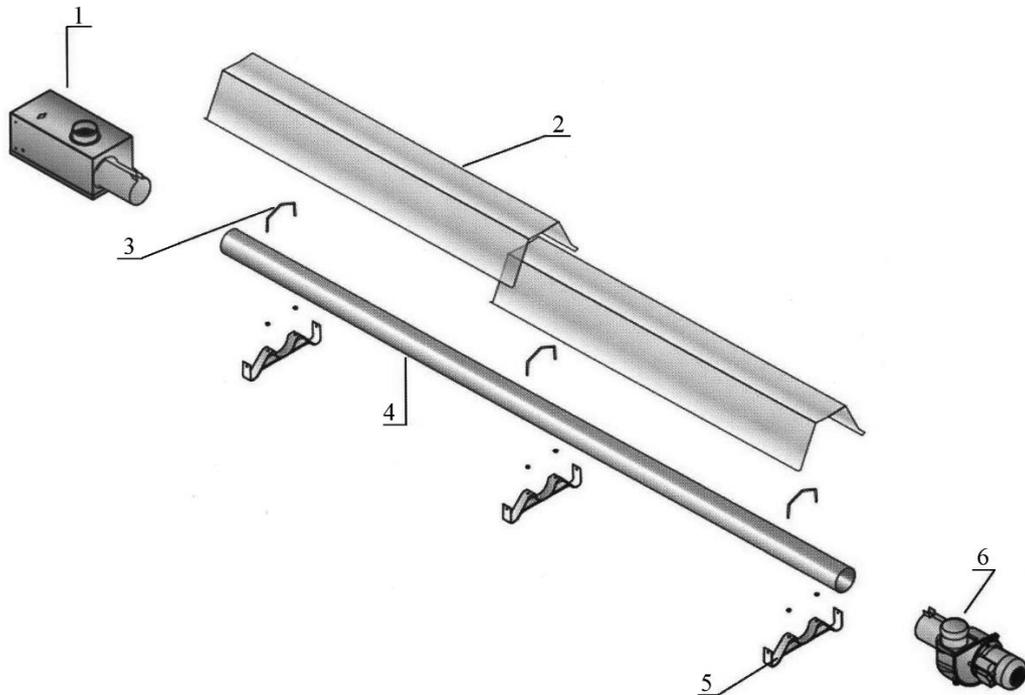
Схема и основные узлы конструкции модульного однотрубного линейного нагревателя INFRA BAF M: 1 – горелочный блок; 2 – рефлектор; 3 – держатель излучающей трубы; 4 – излучающая труба Ø108x2; 5 – опорный кронштейн; 6 – вытяжной вентилятор.
